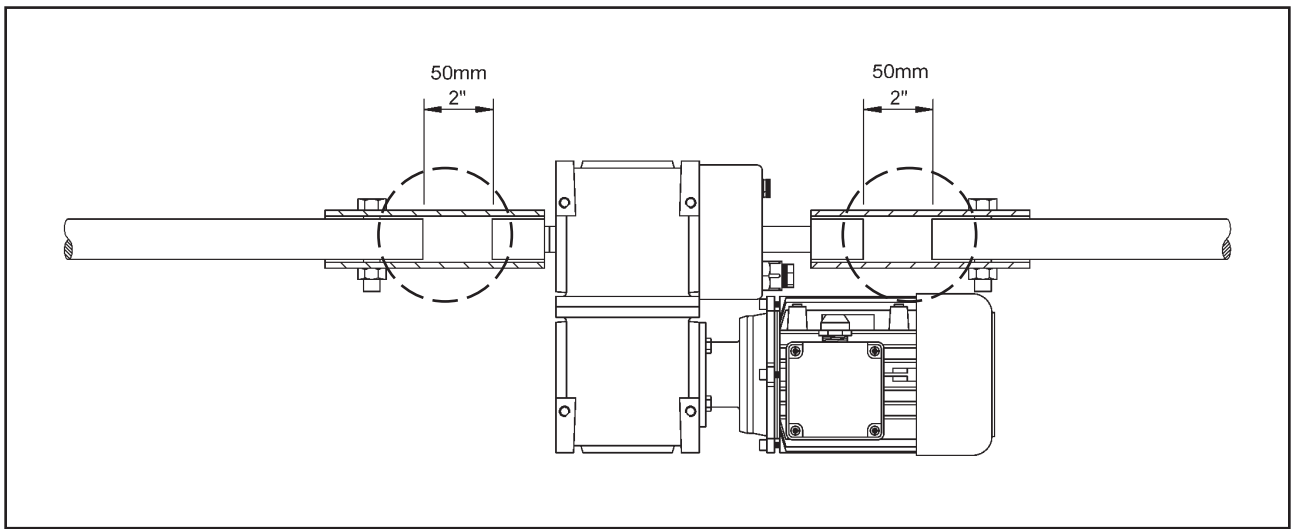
Gearmotor monteret med profilrørskoblinger.
